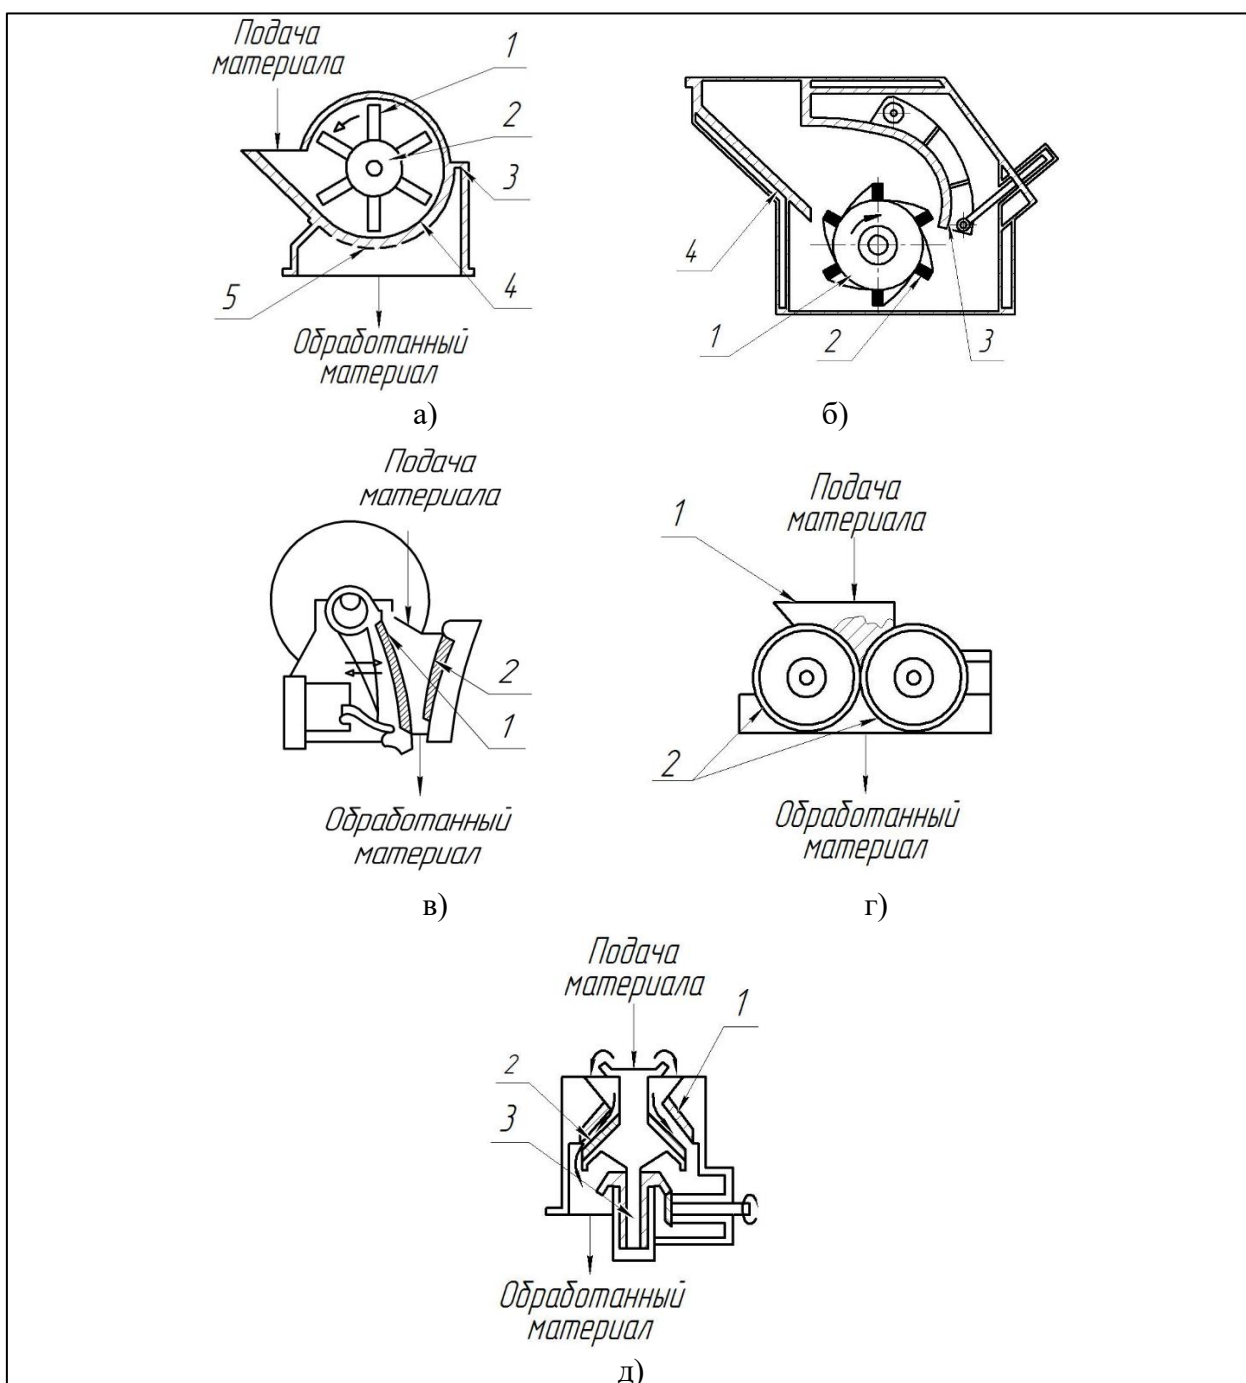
Схемы дробилок: а) 1 – рабочий орган (молотки), 2 – ротор, 3 – корпус, 4 – дека, 5 – решето; б) 1 – ротор, 2 – рифли, 3 – дека, 4 – корпус; в) 1 – неподвижная щека, 2 – подвижная щека; г) 1 – бункер, 2 – вальцы; д) 1 – неподвижный конус, 2 – подвижный конус, 3 – вал.
